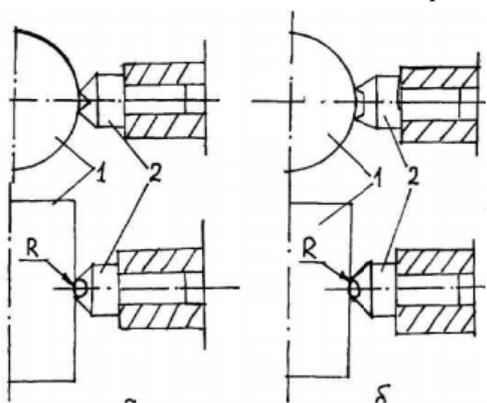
Схема установок выглаживателей при обработке цилиндрической поверхности: а – сферическая форма заточки, б – цилиндрическая
